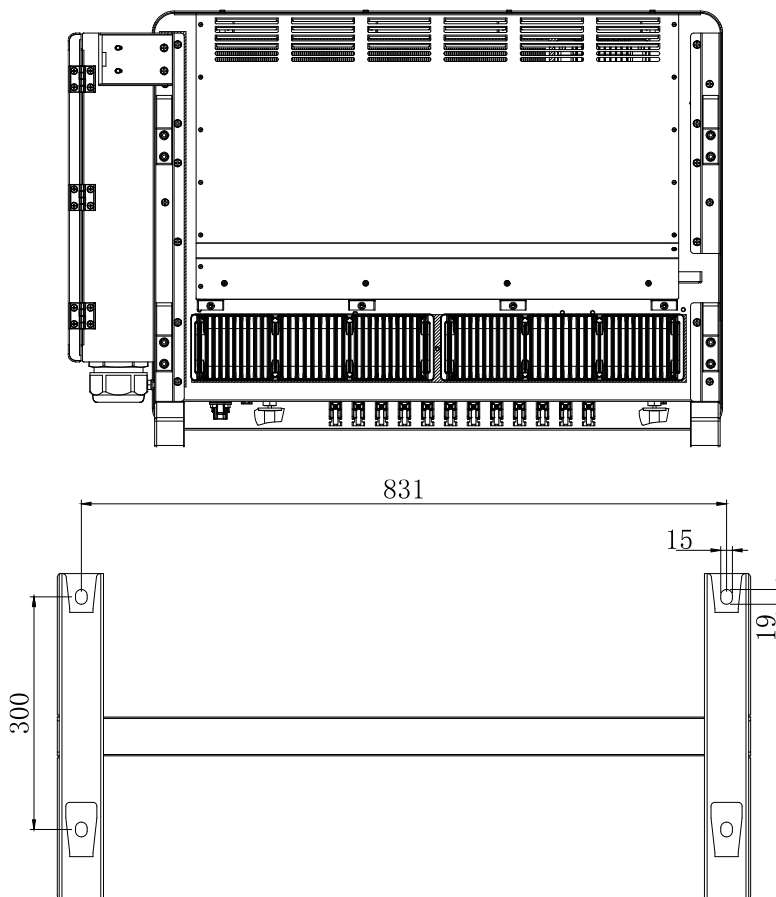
Vista trasera del producto y dimensiones del soporte
